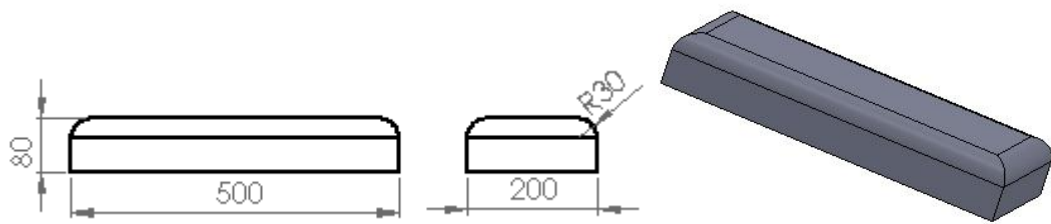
Dimensões e vista isométrica da matriz superior (em milímetros).
